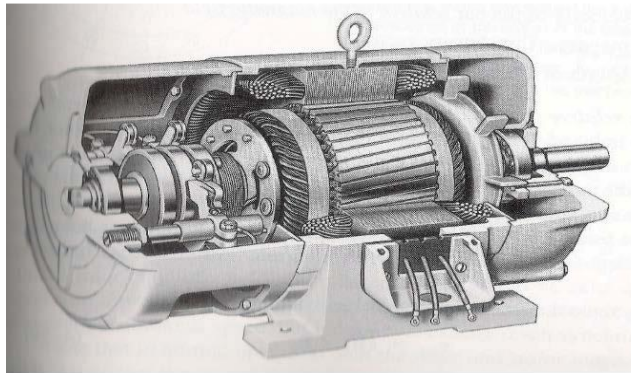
24. Machine asynchrone à rotor bobiné [22]
